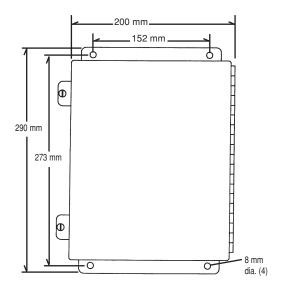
Dimensión de montura – Sensor de altura inicial
